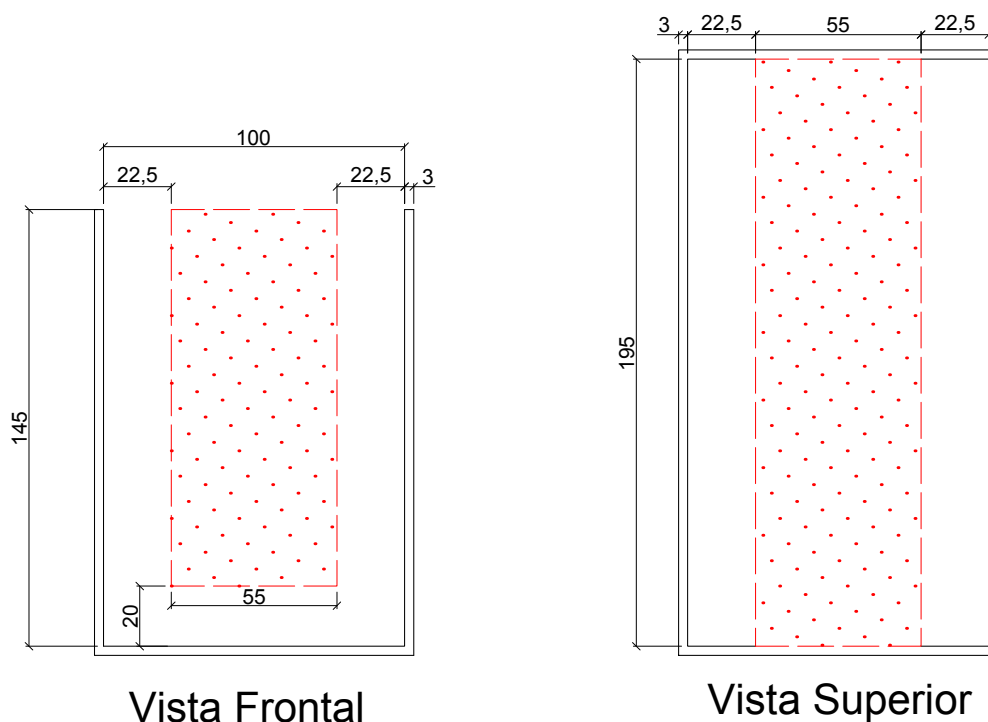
Dimensões geométricas de projeto do ACLS
